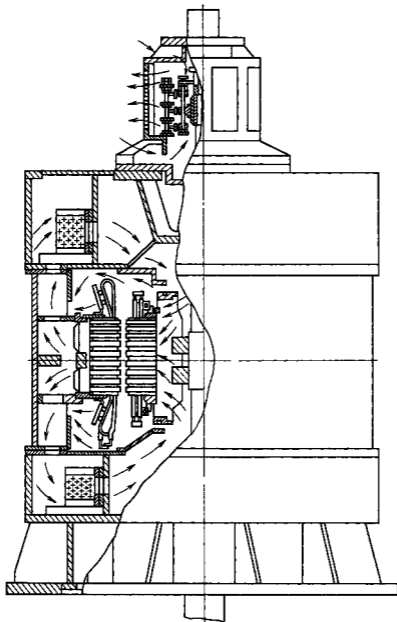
17 Асинхронный вертикальный двигатель типа ВАКЗ
